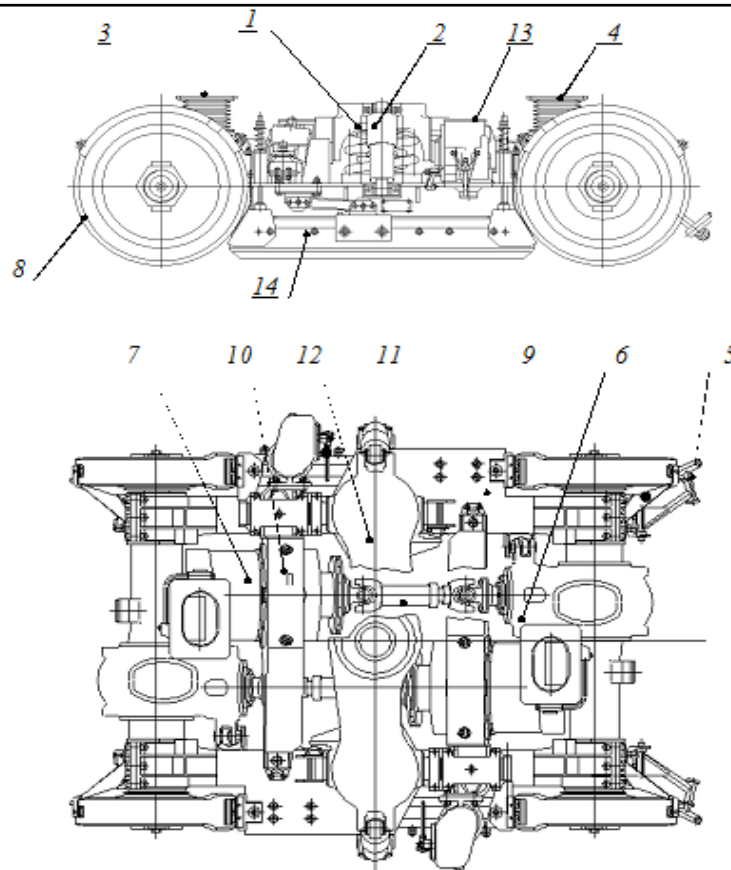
Візок трамвайного вагона «Спектр»: 1 - циліндрична пружина; 2 – гідравлічний гаситель коливань (амортизатор); 3 – вентиляційний кожух; 4 – крила; 5 – патрубок пісочниці; 6 – редуктор; 7 – тяговий двигун; 8 – колесо; 9 – поздовжня балка; 10 – поперечна балка; 11 – карданий вал; 12 – надресорна балка; 13 – електромагнітний привід рейкового гальма; 14 – рейкове гальмо
